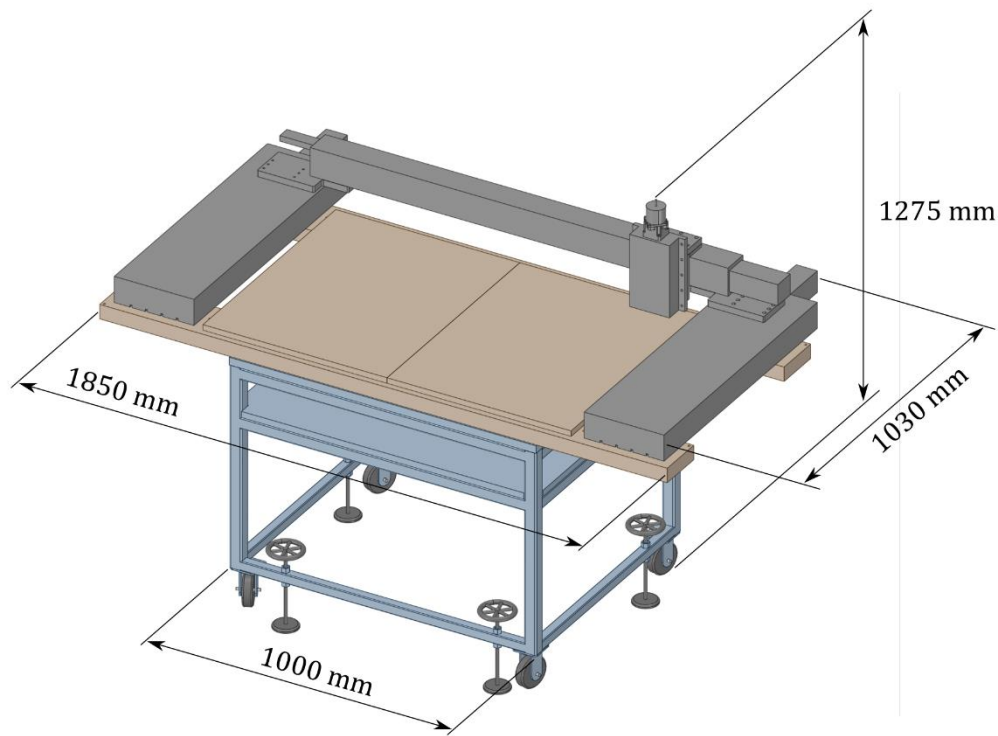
CAD tridimensional del ensamblaje entre la estructura del banco y la cortadora láser
